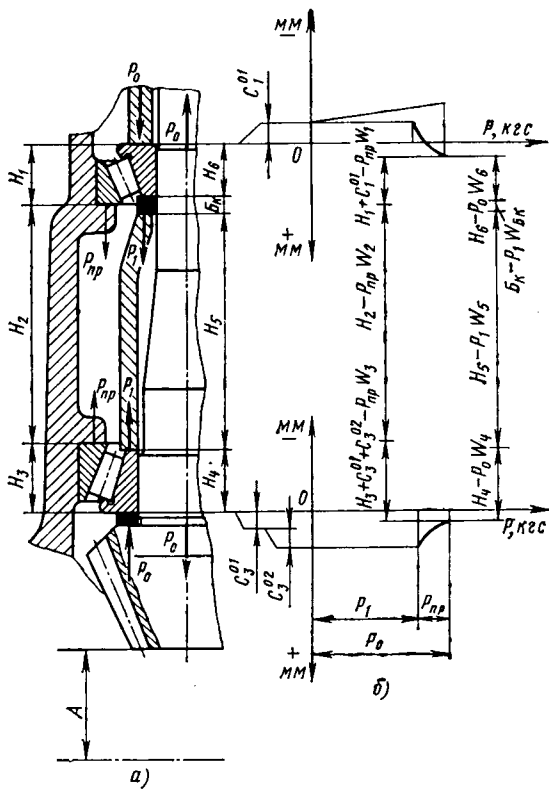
Схема расчета сборочной размерной цепи на преднатяг подшипников ведущей шестерни редуктора: а — конструктивная размерная цепь; б — технологическая сборочная размерная цепь с динамико-силовым замыканием
